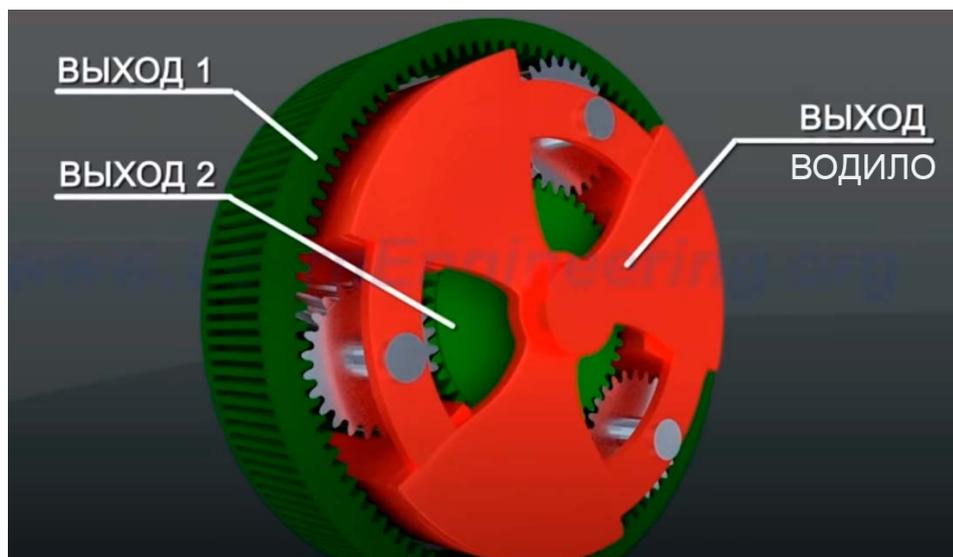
схема передачи крутящего момента в планетарном редукторе.
